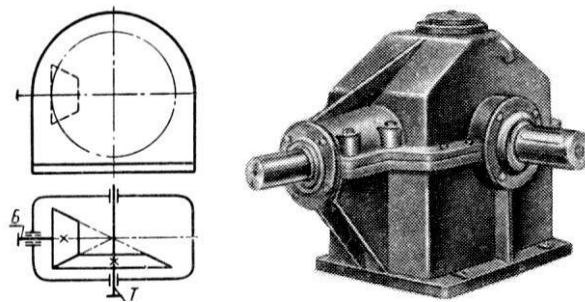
Одноступінчатий редуктор з конічними зубчастими колесами
